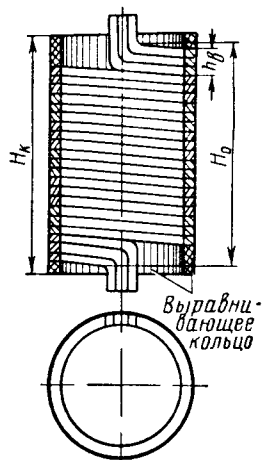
Цилиндрическая слоевая обмотка в разрезе. Положение выравнивающего кольца
